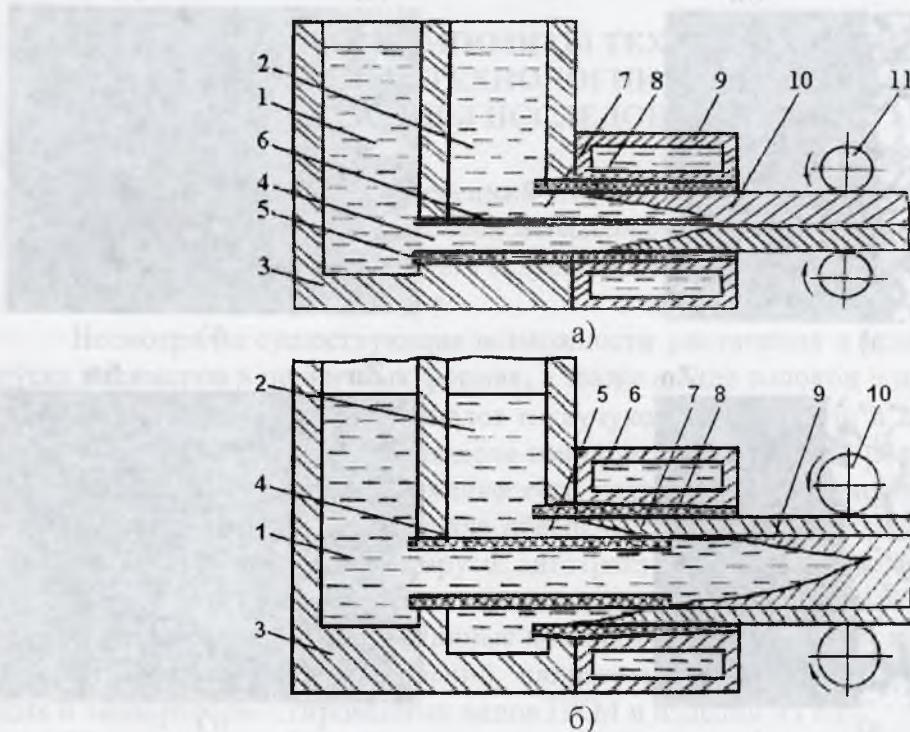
(а) Схема установки для получения прямоугольных биметаллических заготовок: 1 – металл 1; 2 – металл 2; 3 – металлоприемник; 4 – нижний канал; 5 – нижняя графитовая вставка; 6 – пластина; 7 – верхний канал; 8 – верхняя графитовая вставка; 9 – водоохлаждаемый корпус кристаллизатора; 10 – биметаллическая отливка; 11 – тянувшие клети. (б) Схема установки для получения цилиндрических биметаллических заготовок: 1 – металл 1; 2 – металл 2; 3 – двухсекционный металлоприемник; 4 – металлопровод; 5 – кольцевой канал; 6 – водоохлаждаемый корпус кристаллизатора; 7 – полая заготовка металла 2; 8 – графитовая втулка; 9 – биметаллическая отливка; 10 – вытягивающее устройство
